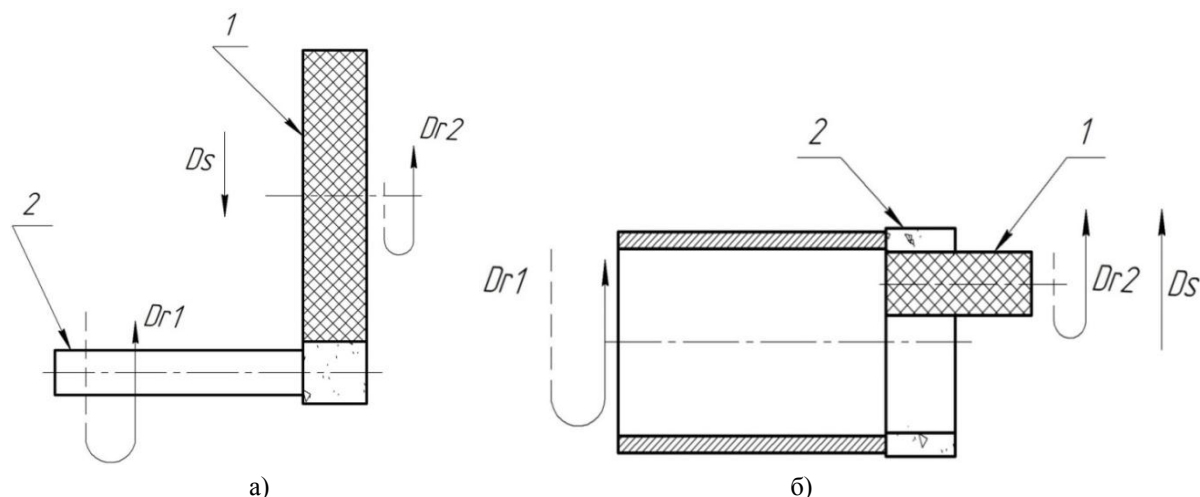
Схема правки алмазных кольцевых сверл абразивным кругом:
